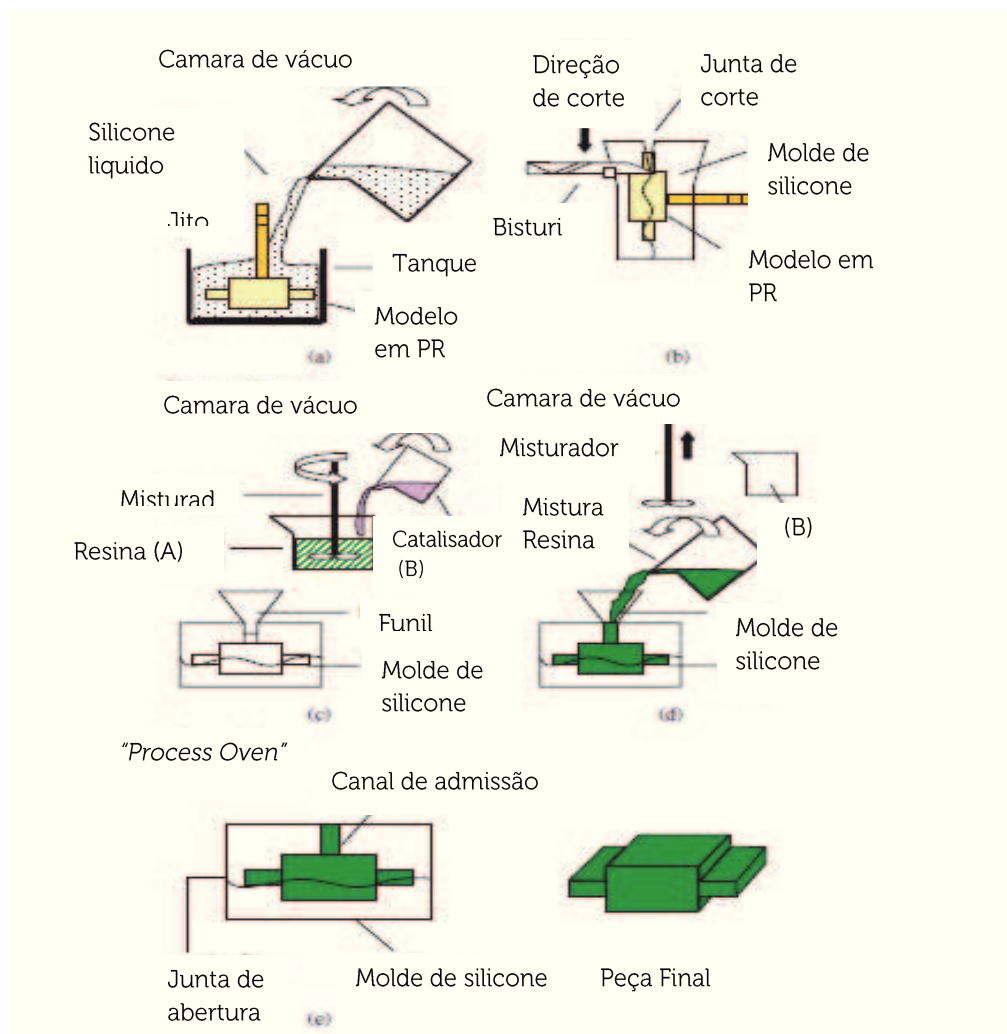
obtenção da Ferramenta rápida por o molde protótipo em silicone Vacuum Casting
